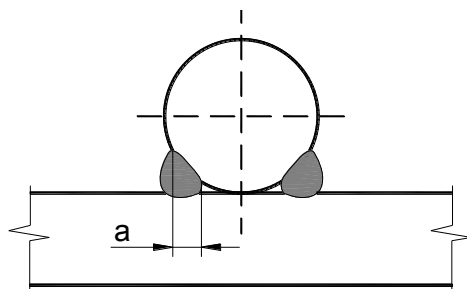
Эффективная высота сварного шва с конусным зазором
